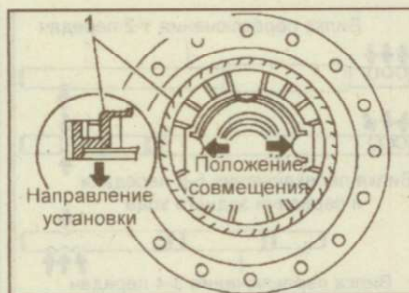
Установочное положение шестерни (1) привода спидометра
